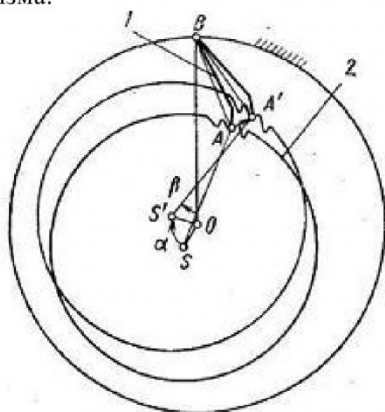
Схема принципа действия корпусного зубчатого преобразующего механизма
